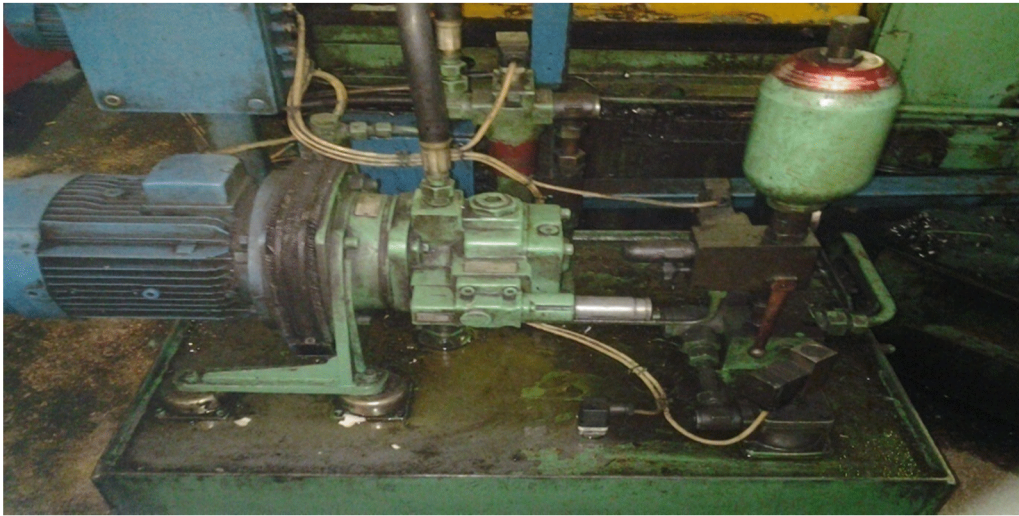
Partie hydraulique de la machine déburreuse OAM.
